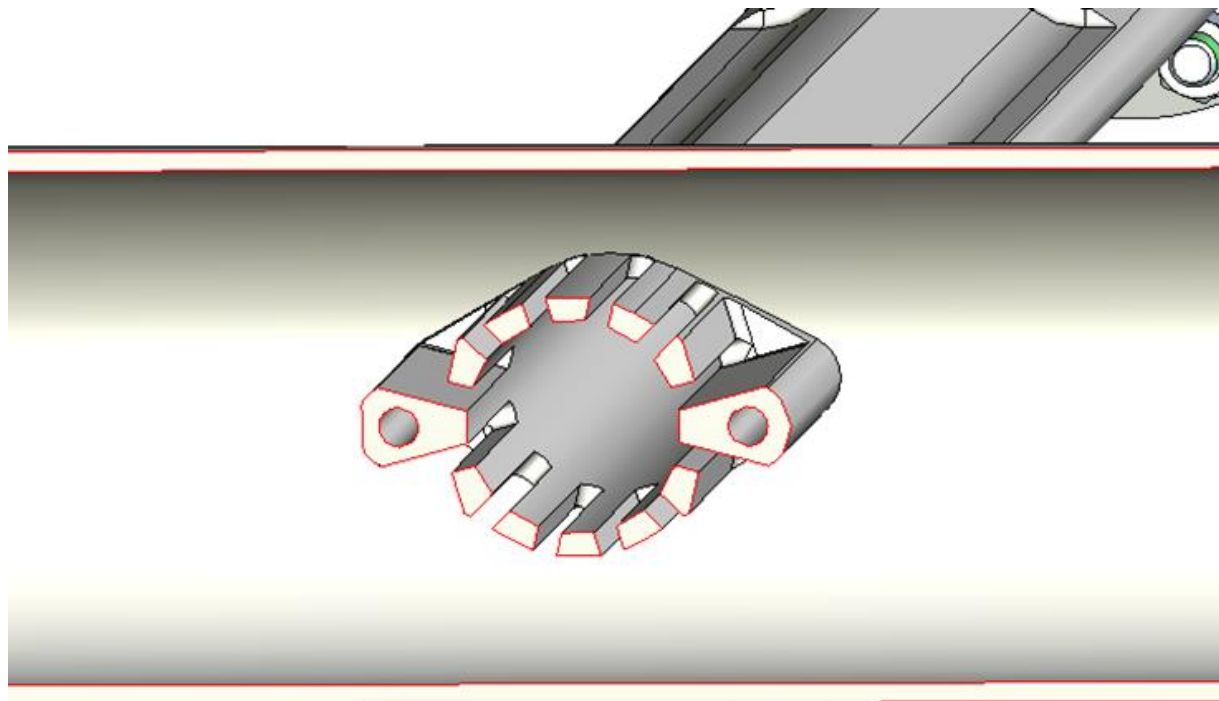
Схема конструкции фланцевого соединения вакуумной камеры накопителя СКИФ
